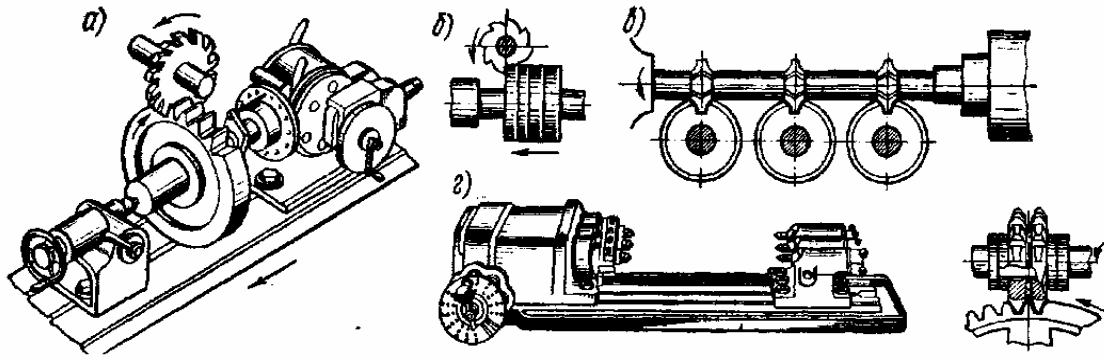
Нарезание зубьев зубчатых колес дисковыми модульными фрезами: *a* – одной заготовки; *б* – нескольких заготовок на одной оправке; *в* – тремя фрезами одновременно; *г* – с применением трехшпиндельной головки; *д* – одновременно двумя модульными фрезами
